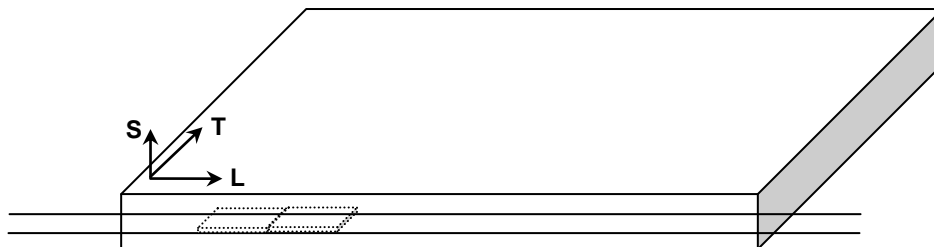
Plan de prélèvement des plaquettes au cœur de la tôle mère en 304L.
